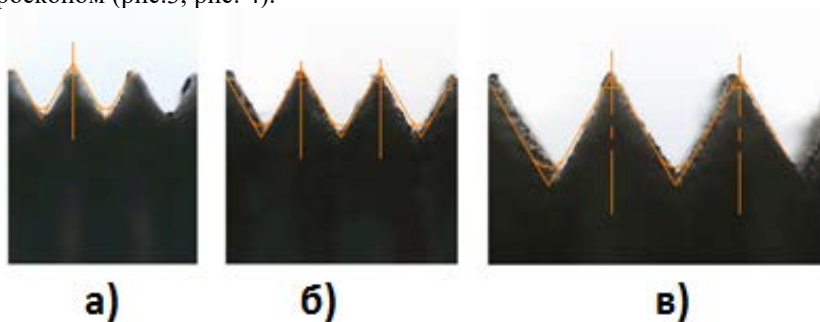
Теоретический и напечатанный профили резьбы: а) М6х1; б) М8х1,25; в) М14х2
